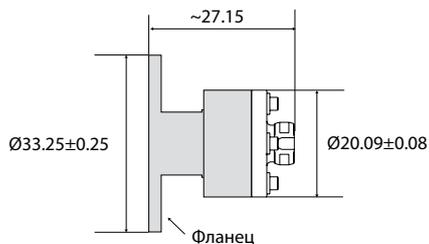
Габаритные размеры фланца коллиматора лазеров моделей FPS10/100 для диаметра пучка 2.1 мм.
